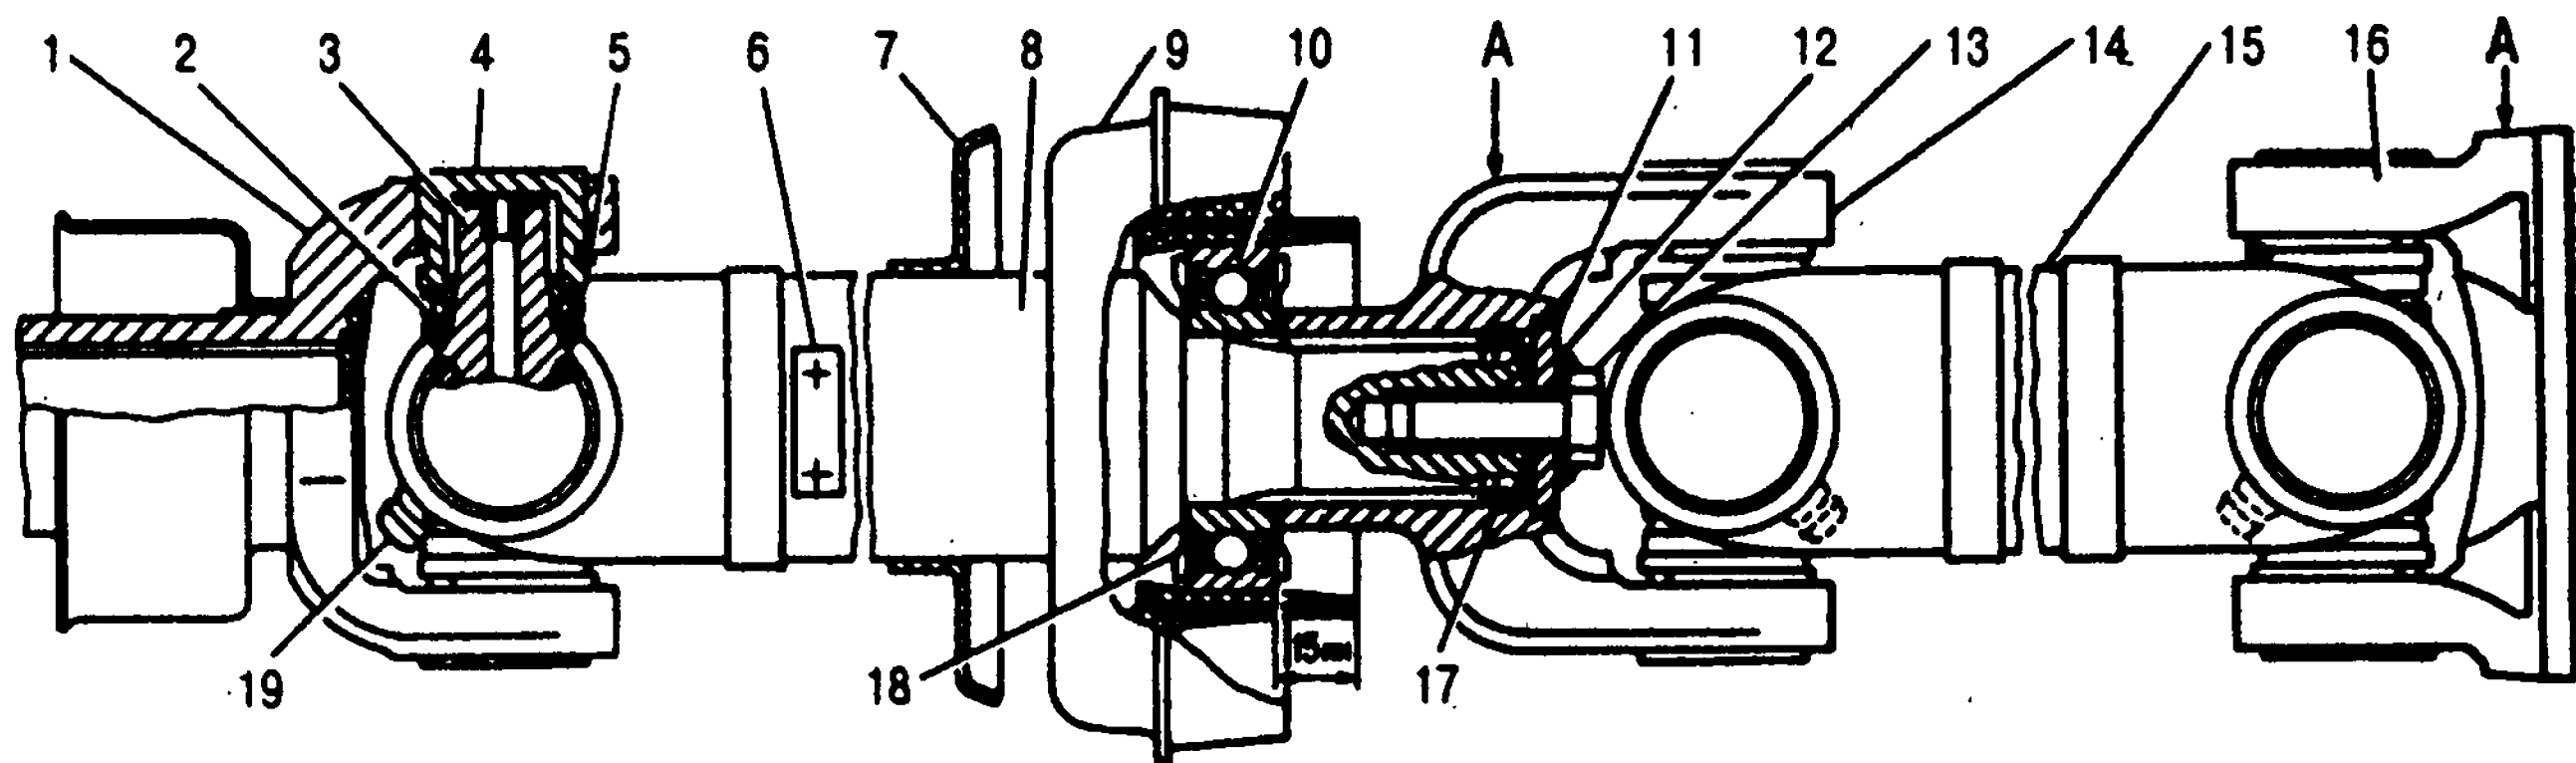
Карданная передача двухвальная: А - место допустимых ударов при демонтаже; 1 - скользящая вилка; 2 - манжета; 3 - крестовина; 4 - игольчатый подшипник; 5 - стопорное кольцо; 6 - балансировочная пластина; 7 - грязеотражатель; 8 - промежуточный карданный вал; 9 - промежуточная опора; 10 - подшипник промежуточной опоры; 11 - П-образная пластина; 12 - стопорная шайба; 13 - болт; 14 - шлицевая вилка; 15 - задний карданный вал; 16 - фланец; 17 - кольцо уплотнительное; 18 - отражатель; 19 - пресс-масленка с колпачком
